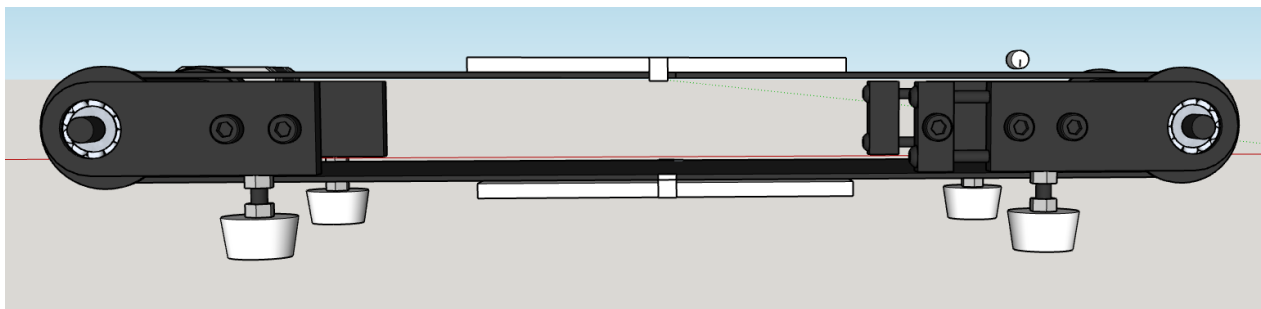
вид збоку на модель конвеєрної стрічки
